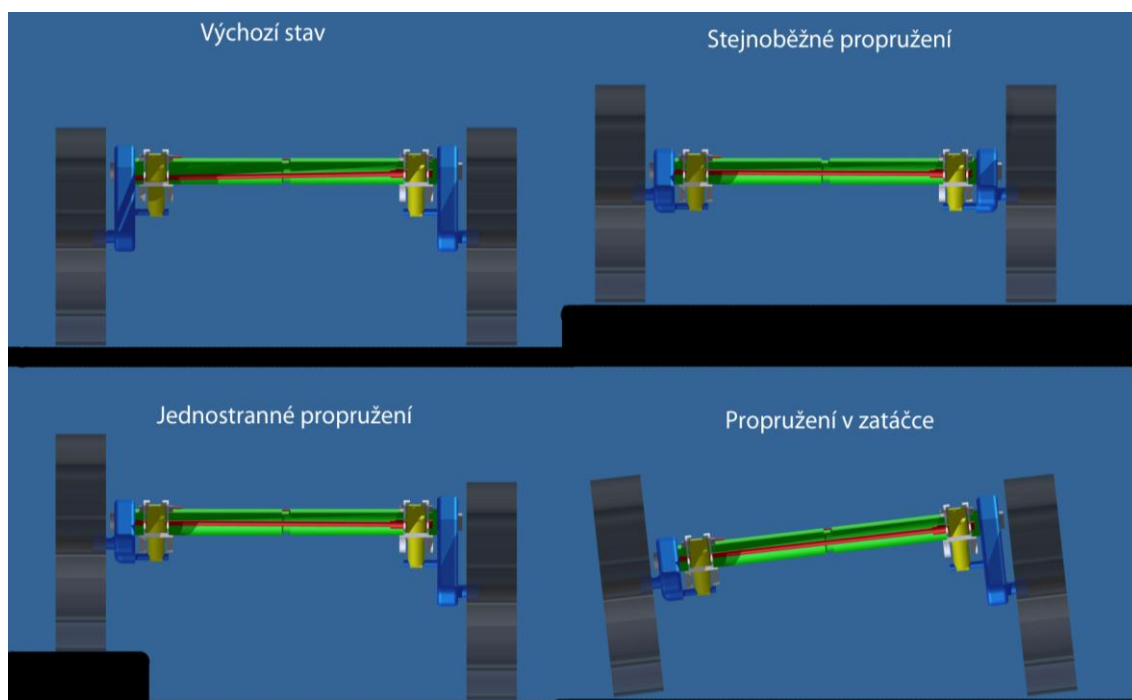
Konstrukce středu klopení klikové nápravy. [1]
